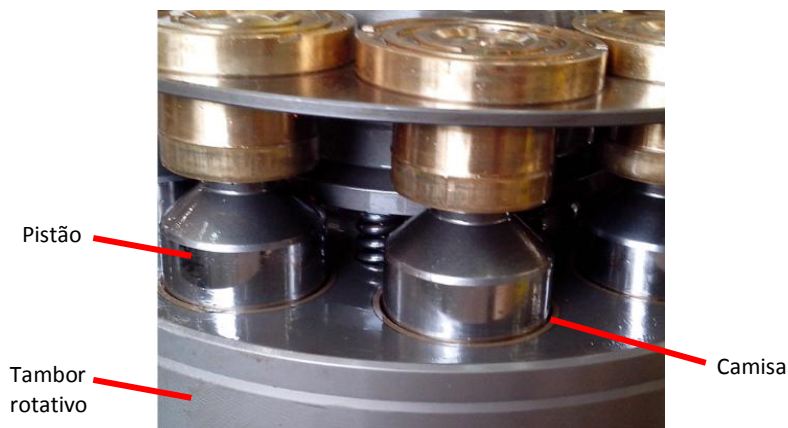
Tambor e pistões de uma bomba de pistão axial.
